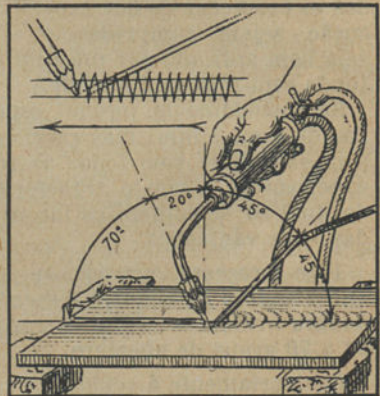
Posição para a execução duma soldadura para traz.
